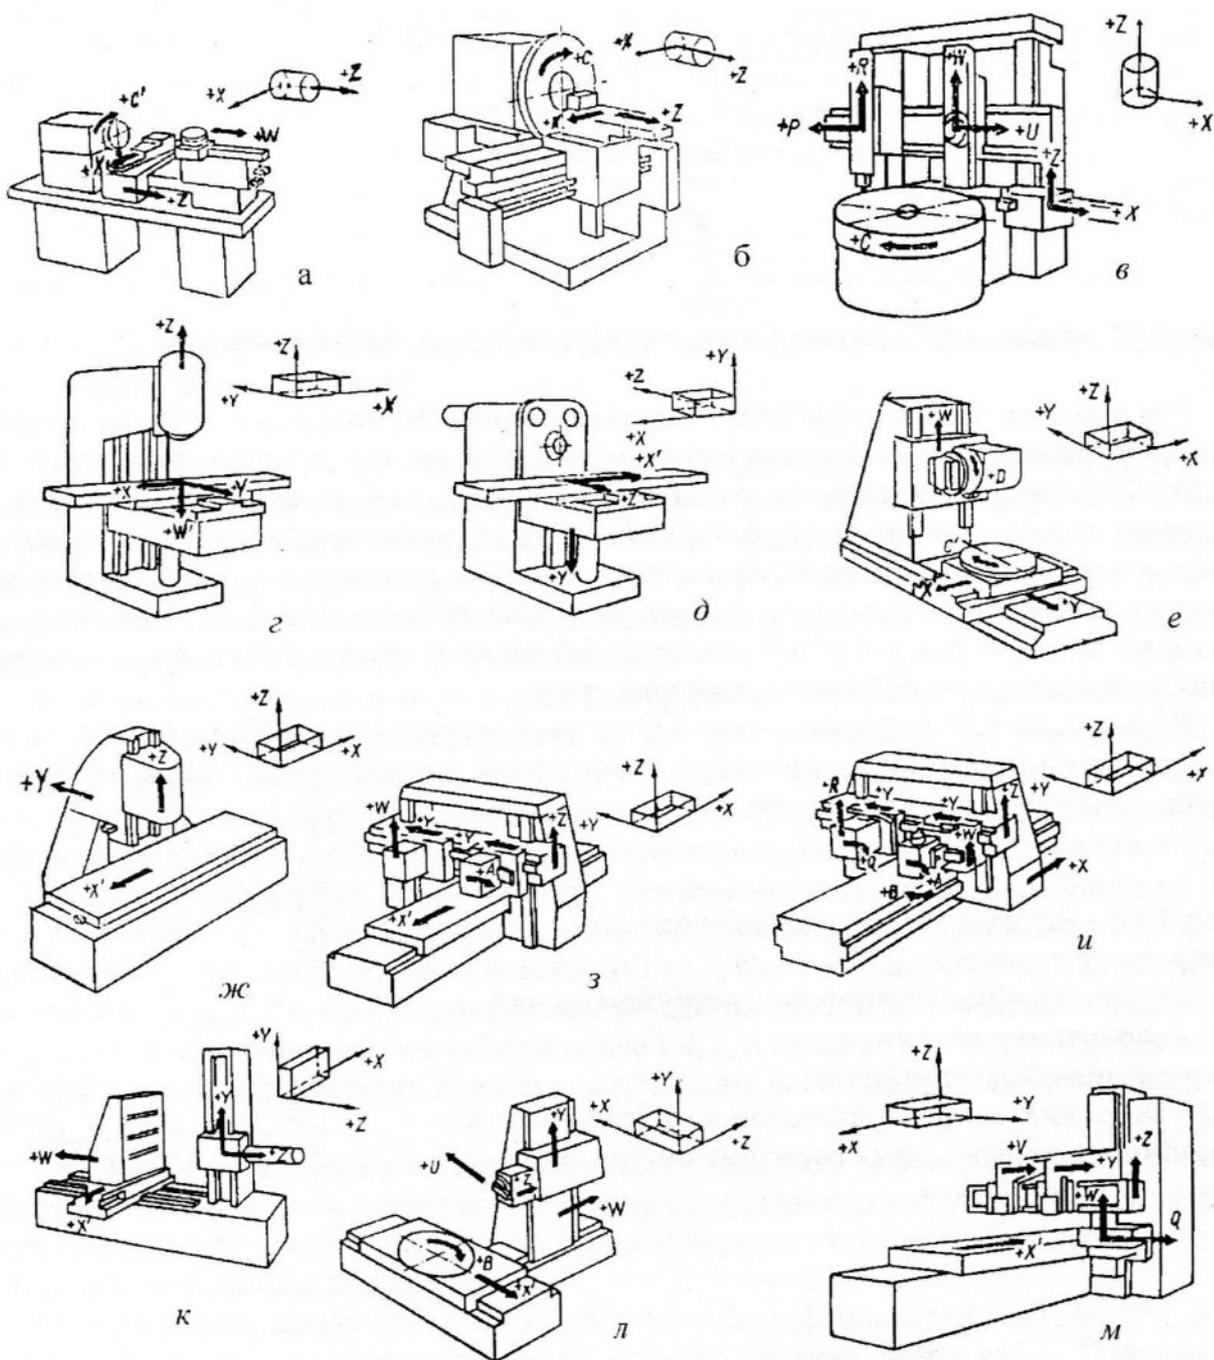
Позначення осей координат і напрямків переміщень на схемах верстатів з ЧПК: а – токарно-револьверного; б – лоботокарного; в – токарно-карусельного; г – вертикально-фрезерного; д – горизонтального консольно-фрезерного; е – фрезерного з поворотним столом і поворотною бабкою; ж – вертикального портално-фрезерного; з – двостійкового портално-фрезерного; и – двостійкового з рухомим порталом; к – горизонтально-розточувального з нерухомою передньою бабкою; л – з поздовжньо-рухомою передньою бабкою; м – поздовжньо-стругального
